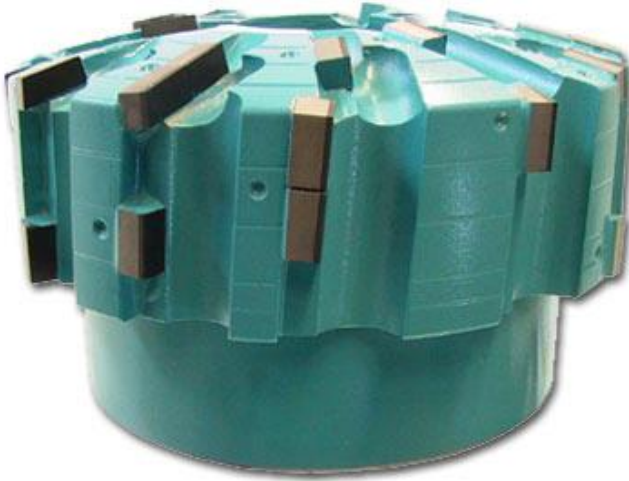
Zulauffräser Gigant Quelle: Hächler Umwelttechnik
